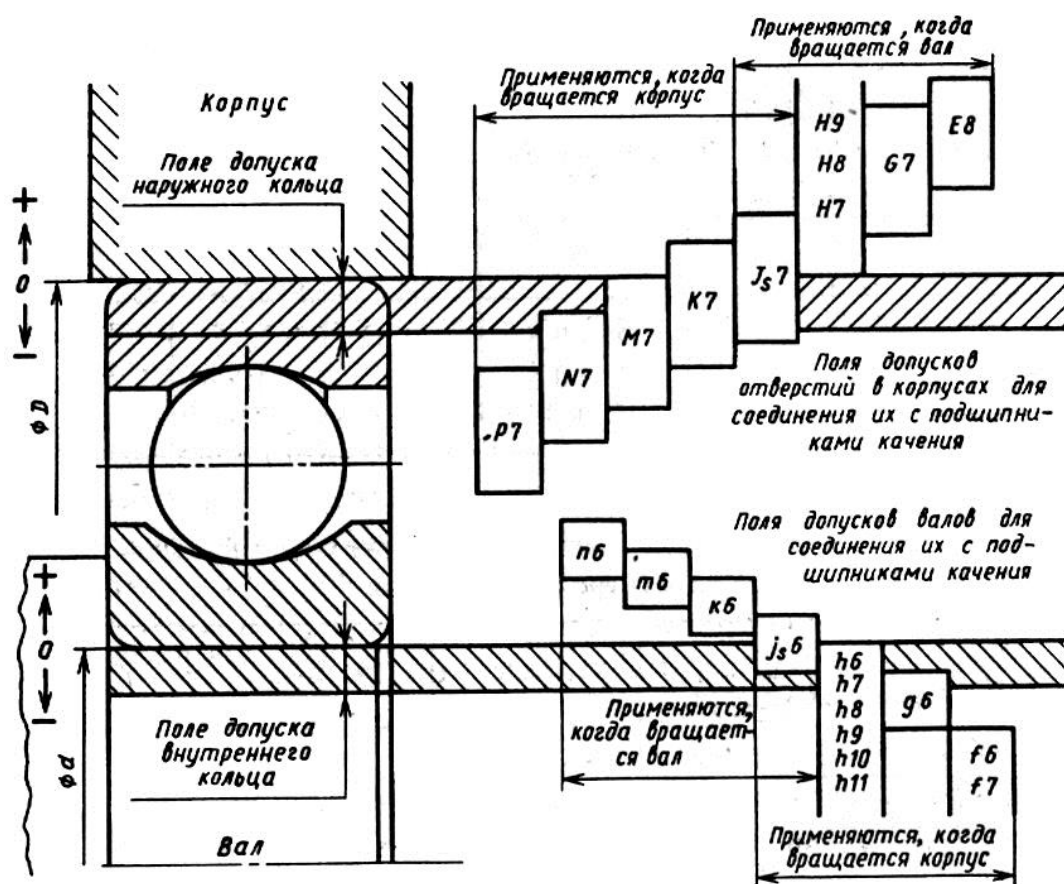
Схема расположения полей допусков подшипника
